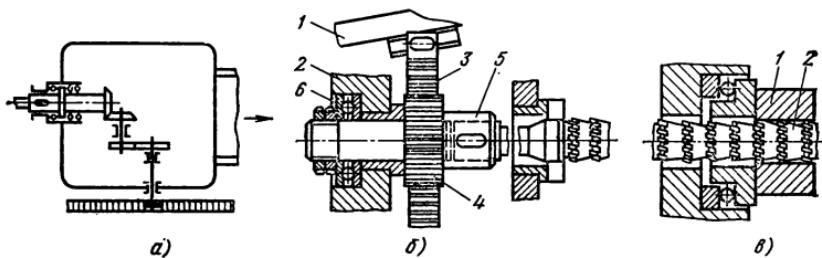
Схемы приспособлений для протягивания винтовых шлицев
